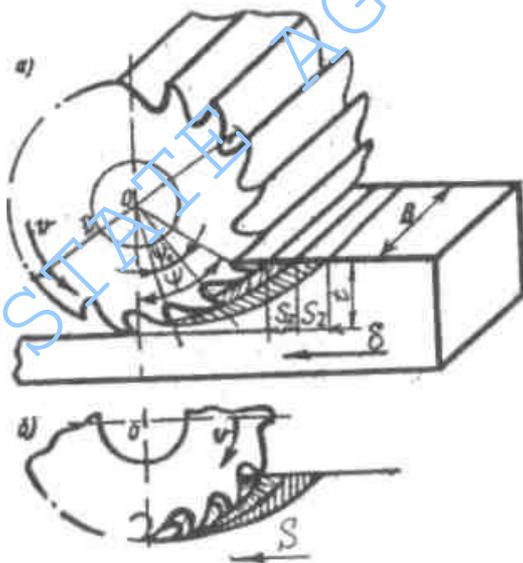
Элементы режима резания при фрезеровании цилиндрической фрезой
